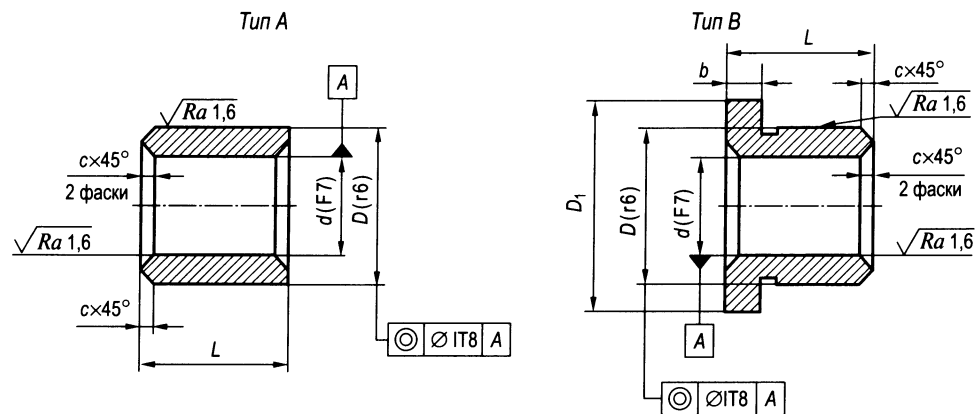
Втулки металлические для подшипников общего назначения
